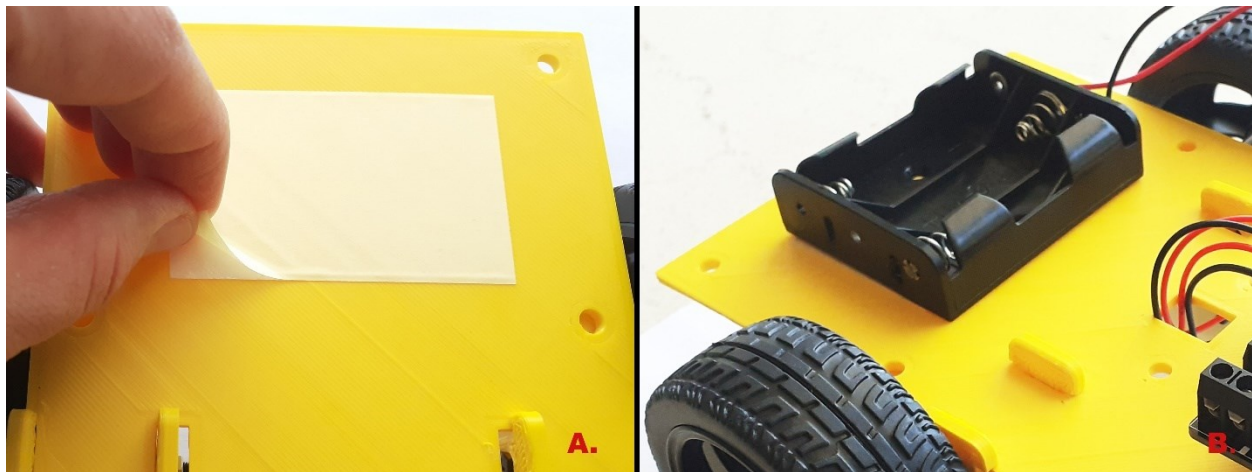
A. Retrait de la partie supérieure du ruban adhésif double face ; B. Fixation du support de piles en place
